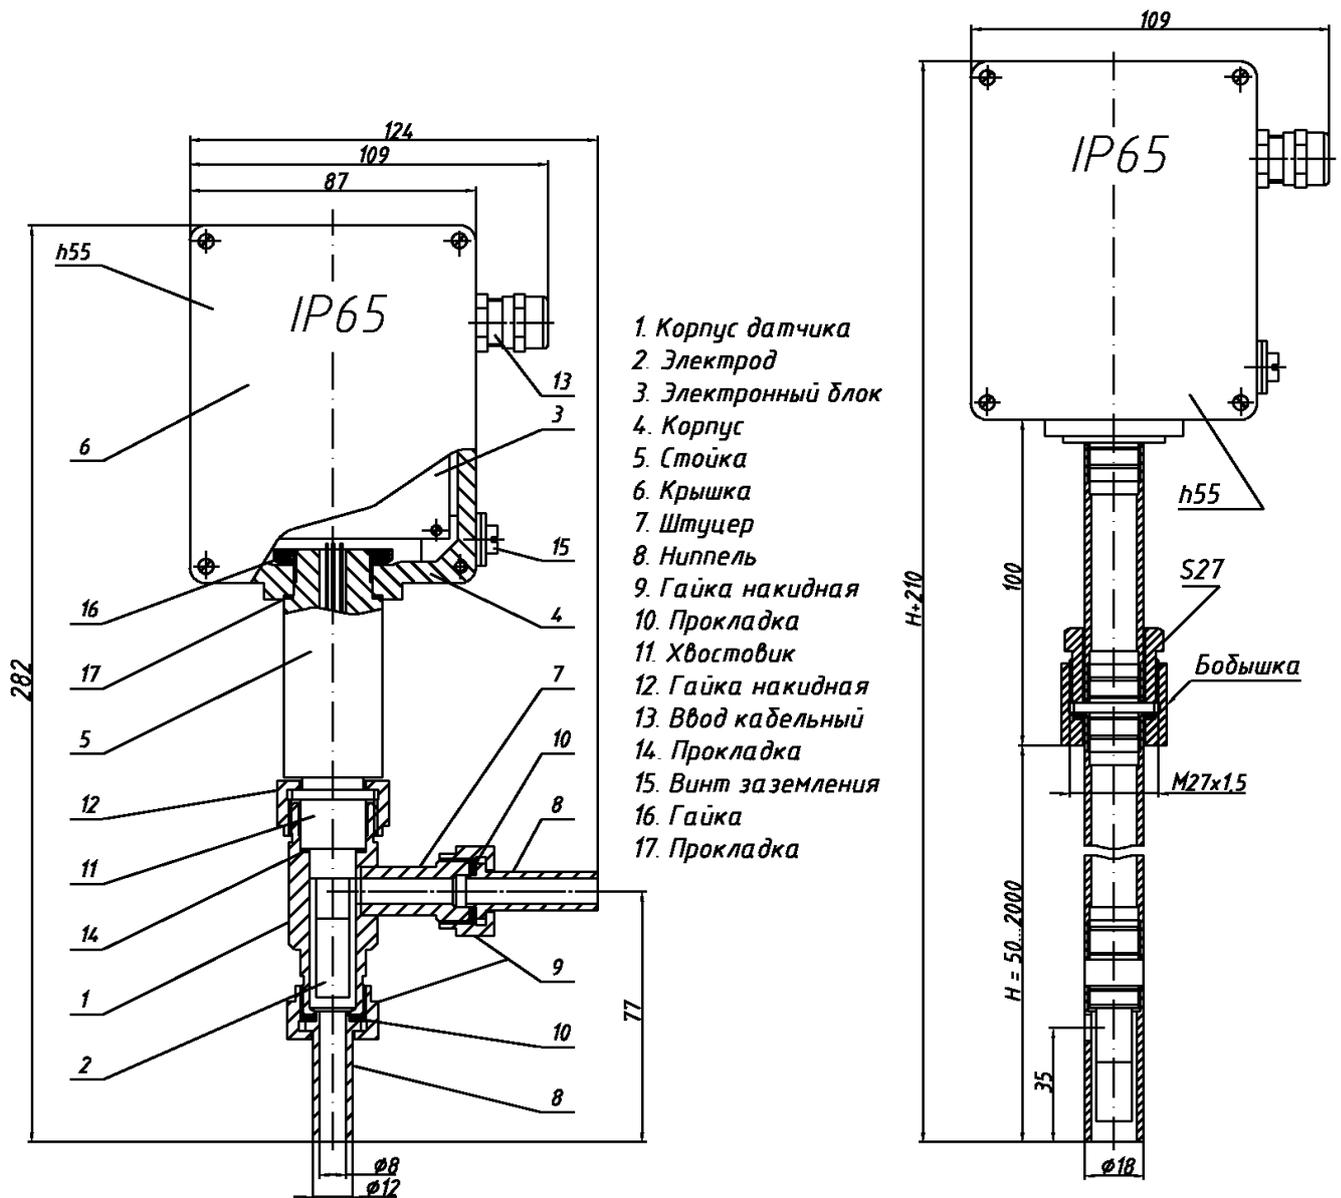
ПП проточного типа с ниппелями под приварку
